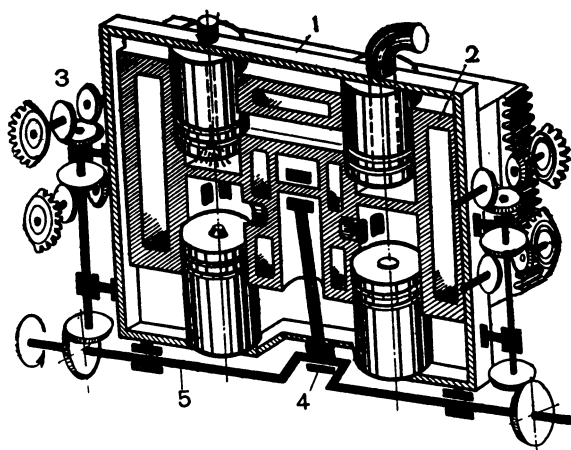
Схема двигателя изобретателей Н. К. Кашуба и И. А. Кораблева:
